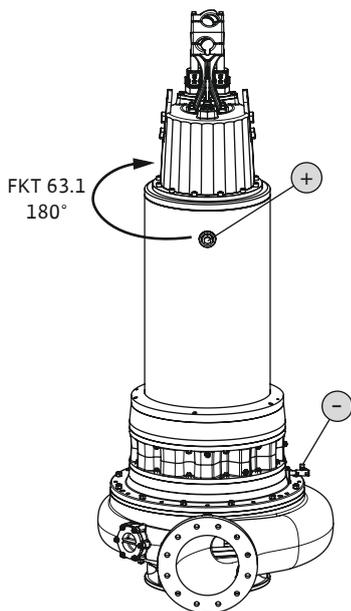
Sistema de refrigeración: Cambio de refrigerante FKT 50.1, 57, 63.1
